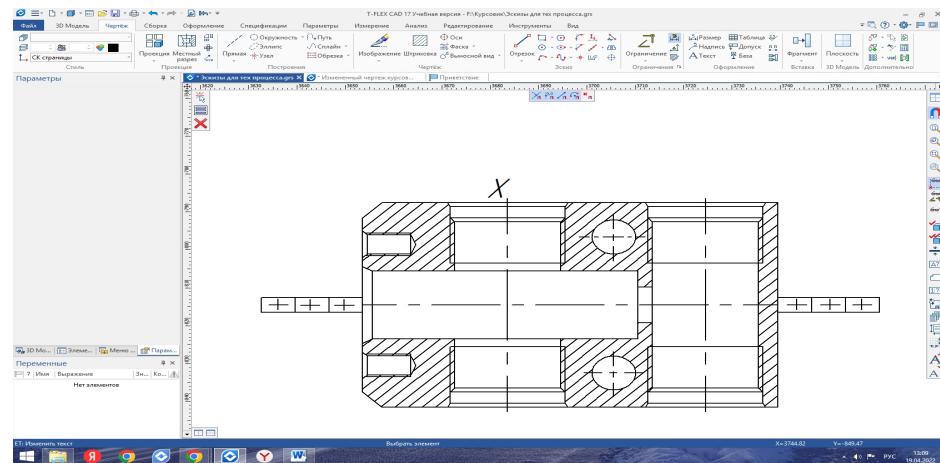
Схема базирования детали ПЛИТА в тисках с призматическими губками
